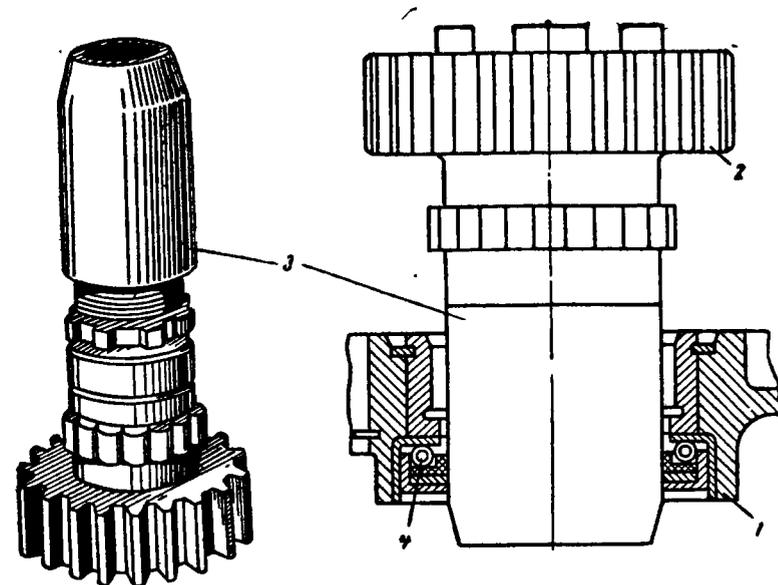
Установка шестерни вторичного вала в коробку передач мотоциклов «ИЖ»: 1 — боковая крышка коробки передач; 2 — шестерня вторичного вала; 3 — вспомогательная трубка; 4 — сальник.
